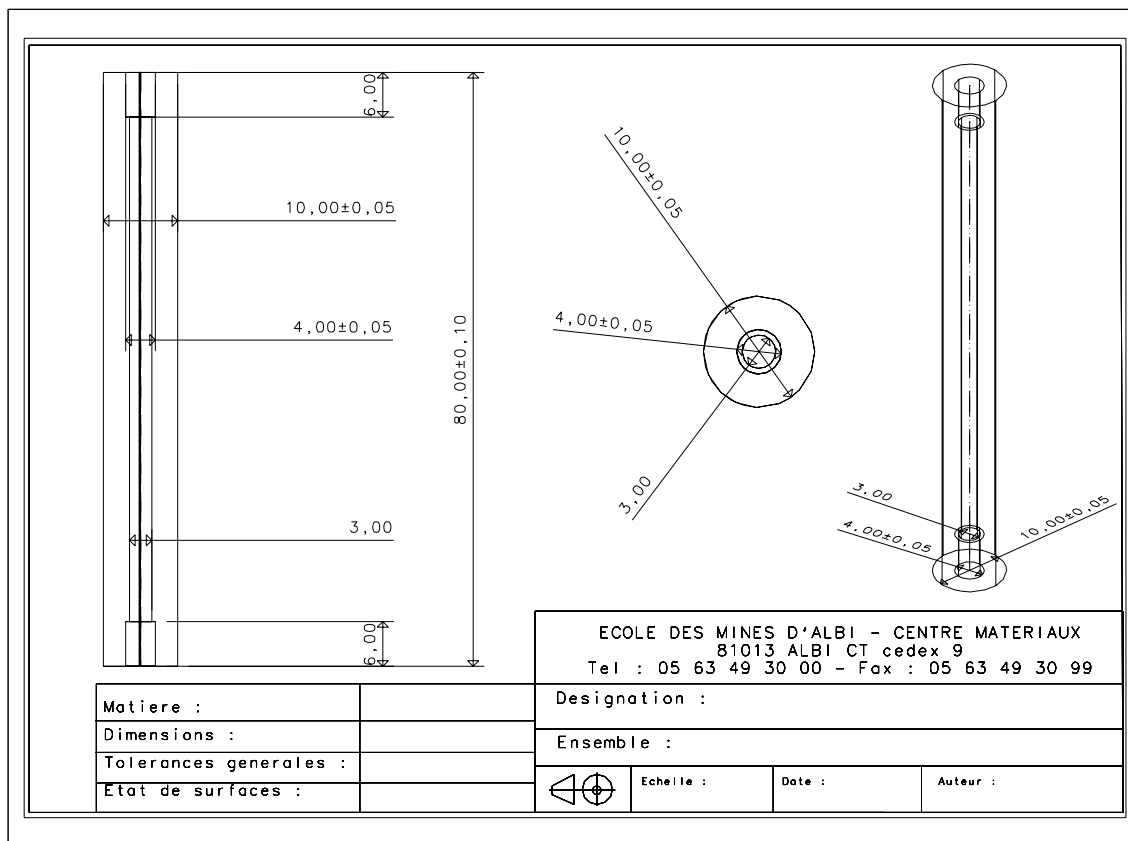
Géométrie de l'éprouvette de fatigue thermique
